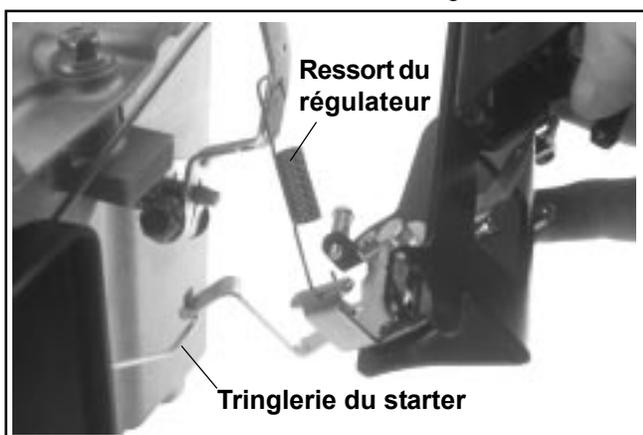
Connexion de la tringle du starter et du ressort du régulateur.
